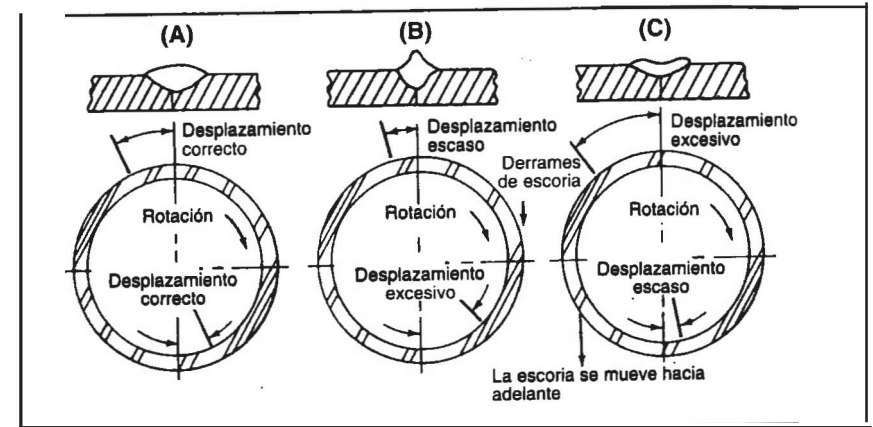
EFECTO DE LAS POSICIONES DEL ELECTRODO SOBRE LA FORMA DEL CORDÓN DE SOLDADURA DURANTE EL SOLDEO CIRCUNFERENCIAL
